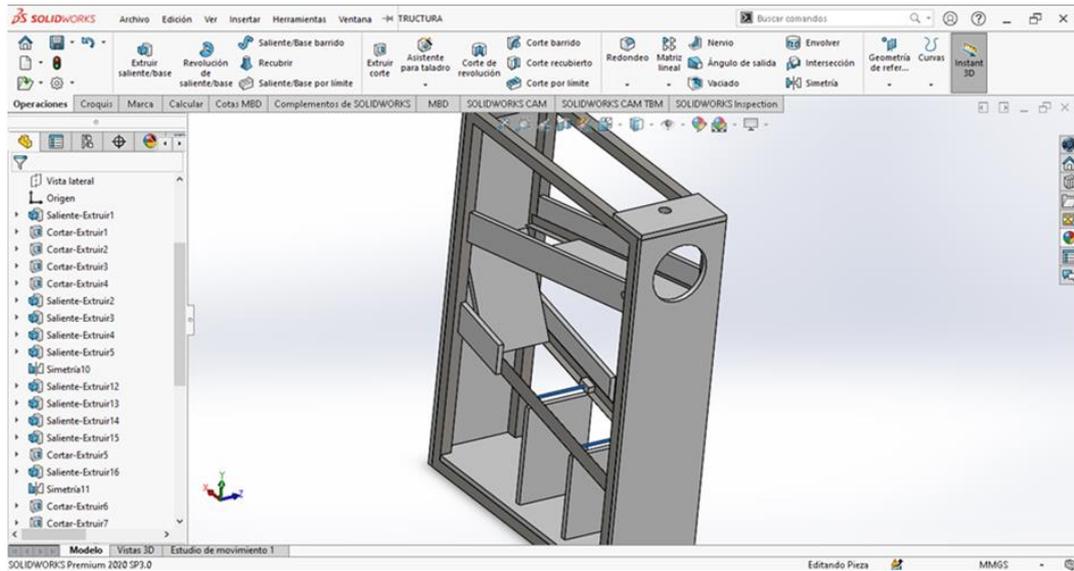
Estructura del proyecto – Solidworks (Vista 2)
